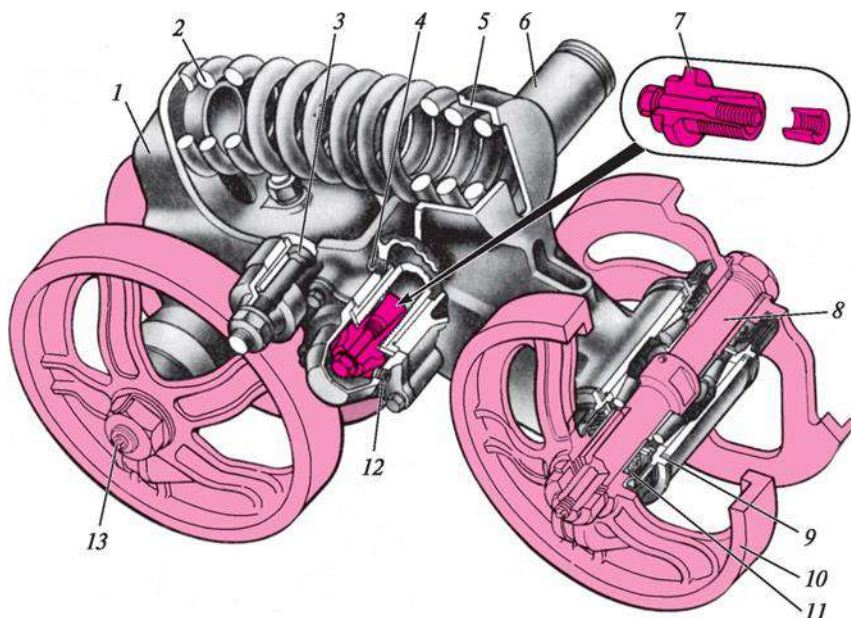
Каретка трактора ДТ-75МЛ: 1, 5 — внутренний и внешний балансиры; 2 — пружина; 3, 8 — оси балансиров и опорных катков; 4, 12 — пробки маслосливного и контрольного отверстий; 6 — цапфа; 7 — кантовая гайка; 9 — регулировочные прокладки; 10 — каток; 11 — уплотнительное устройство; 13 — пробка
